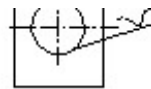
Схема базування та закріплення при фрезеруванні
